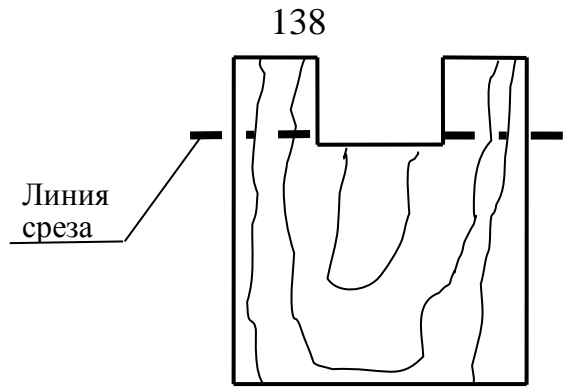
Схема подготовки образцов к измерению твердости
